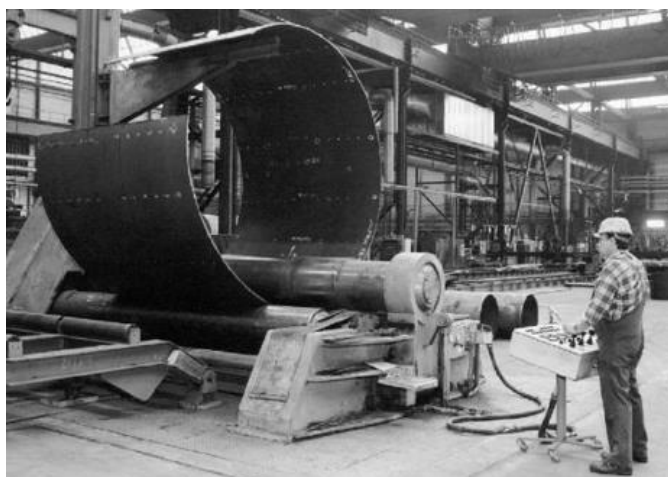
Fabricação da secção da torre, HAU 2006.
